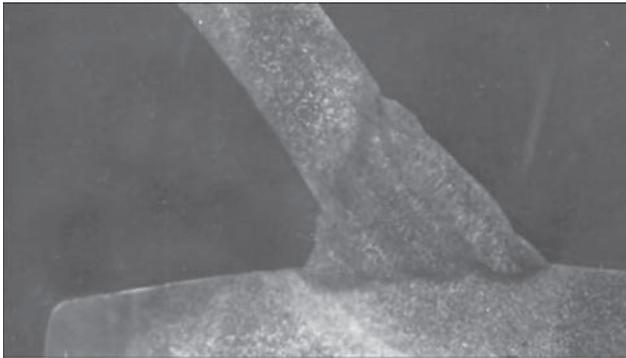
Макрошлиф соединения, выполненного ручной электродуговой сваркой
